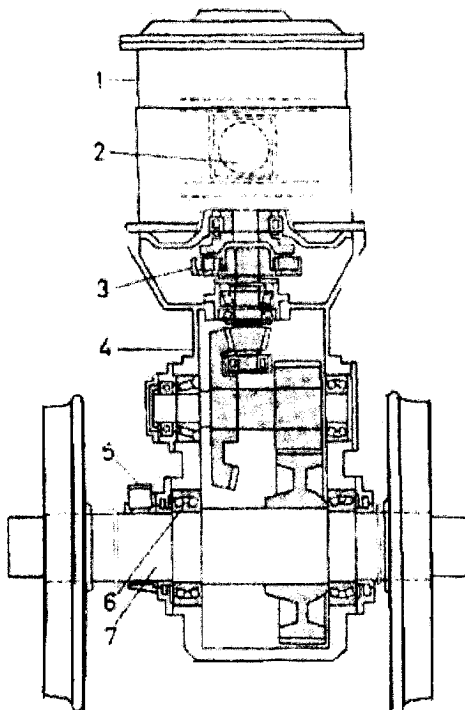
Конструкция подвески тягового двигателя и трансмиссии шахтного электровоза фирмы ASEA (Швеция): 1 – двигатель; 2 – резиновая опора; 3 – эластичная муфта; 4 – редуктор; 5 – скользящий контакт; 6 – роликовый подшипник; 7 – ось колёсной пары
